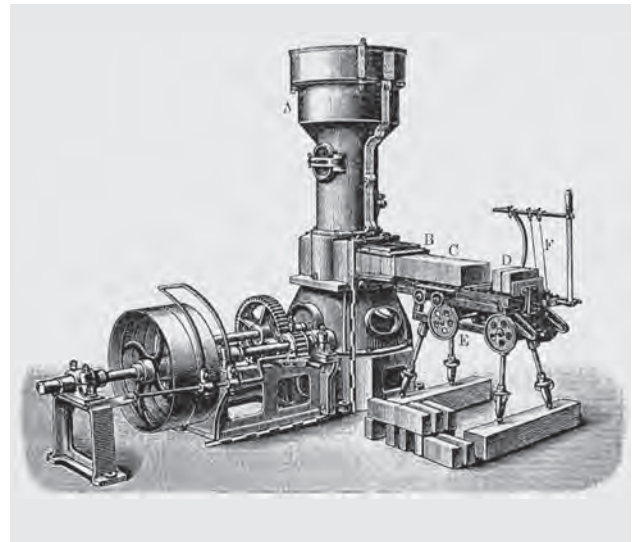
Mit Dampfkraft betriebene stehende Ziegelpresse, um 1890
